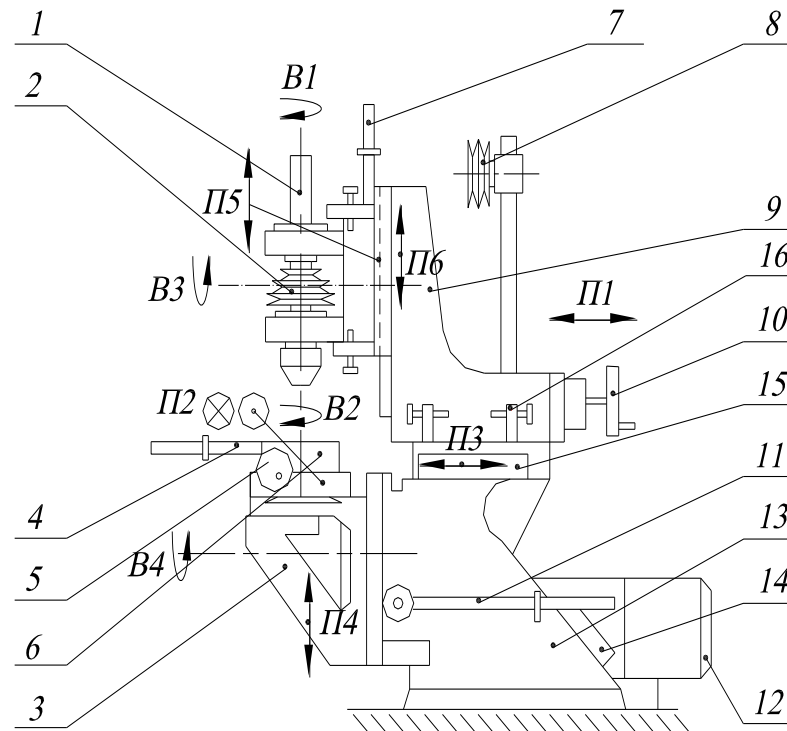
Универсально-фрезерный станок мод. НО-800:
